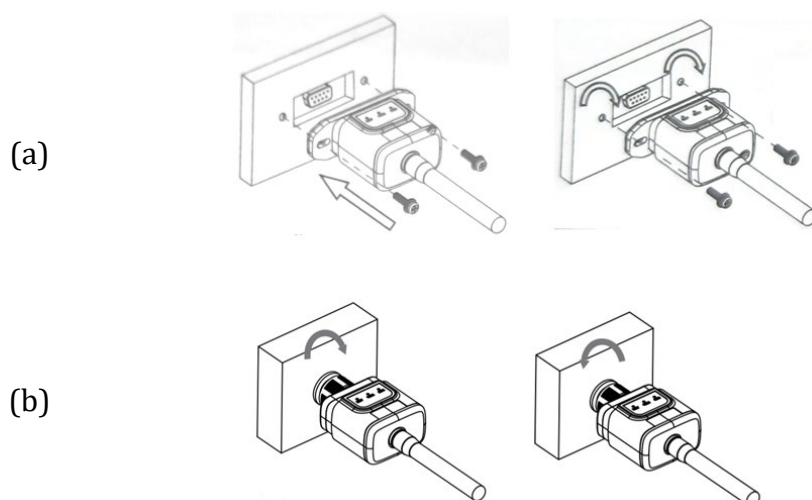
Inserimento e fissaggio dell'adattatore Wi-Fi esterno
